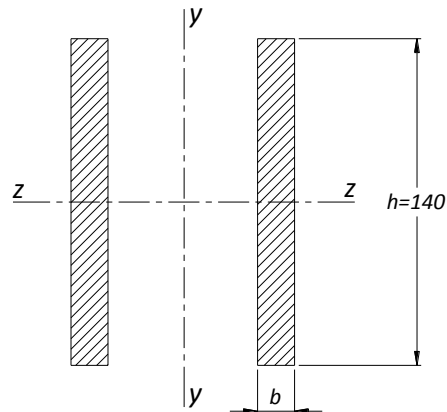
Sección de la viga del brazo de apoyo inferior.
